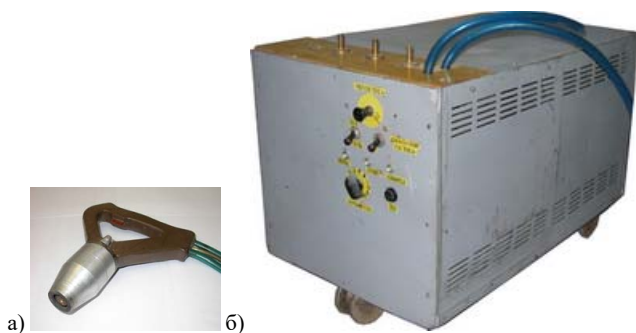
Внешний вид оборудования: *а* – плазматрон для точечной сварки; *б* – установка типа УДГТ-150У2
